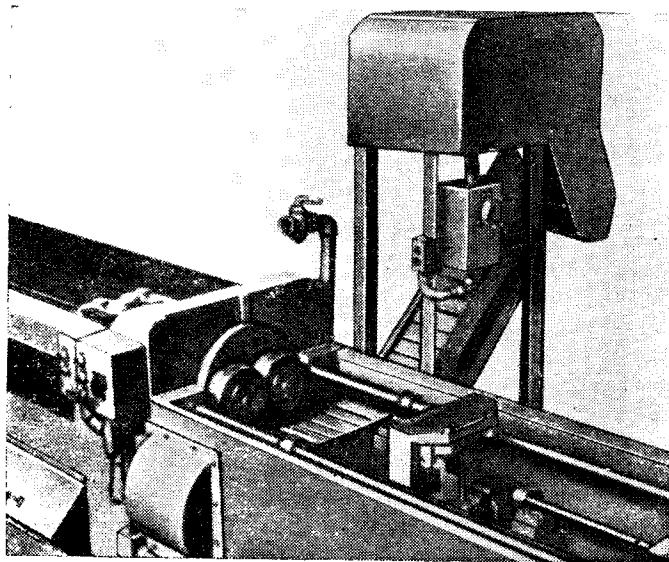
Конвейер для удаления обработанных деталей с горизонтально-протяжного станка
